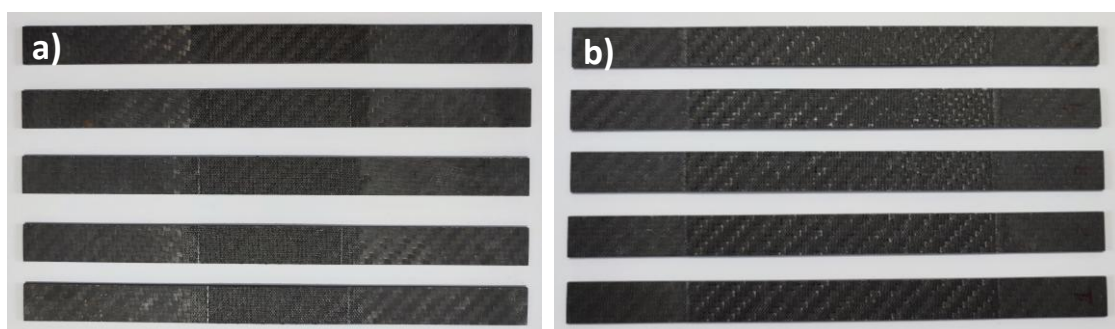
Provetes reparados para ensaio à tração: a) com preenchimento da fissura; b) com substituição das peles danificadas, em formato de escalonado
